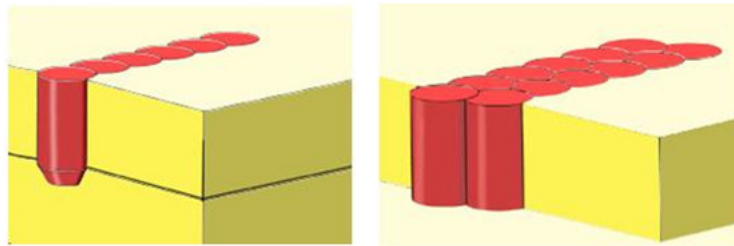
Soldagem a fricção por costura com passes simples e múltiplos.
